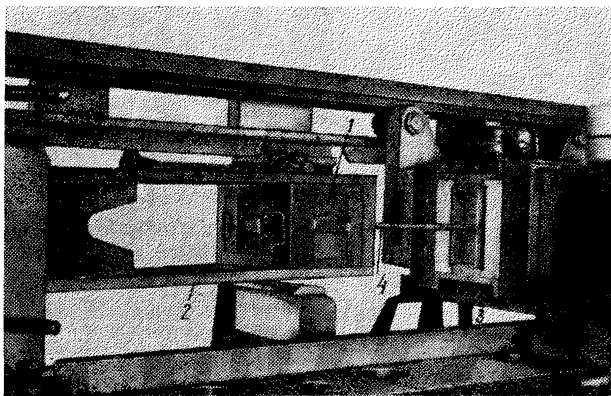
Положение устройства по рис. 22 в процессе испытания сварного соединения
